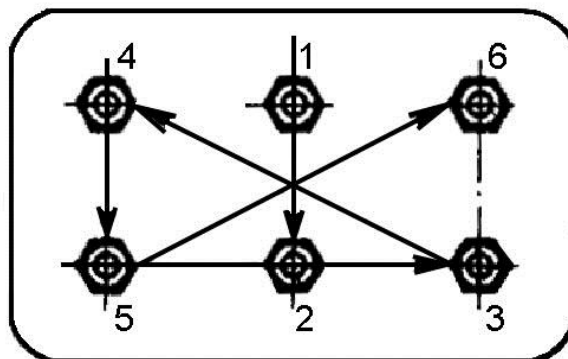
Схема затяжки шпилек крышки цилиндров
